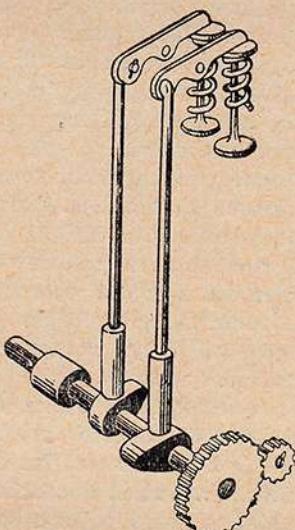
Газораспределительный механизм четырехтактного двигателя.
